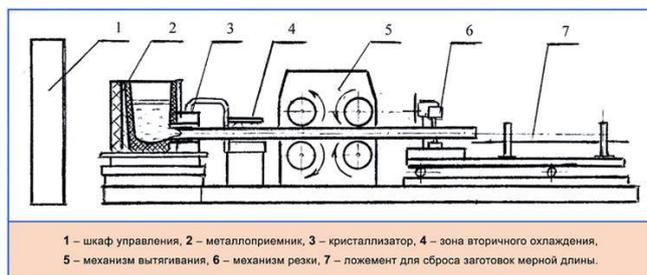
Схема машины непрерывного литья заготовок из цветных металлов МНЛ-140
